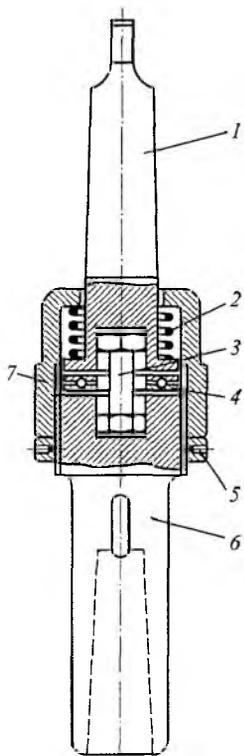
Самоустанавливающийся сверлильный патрон:
